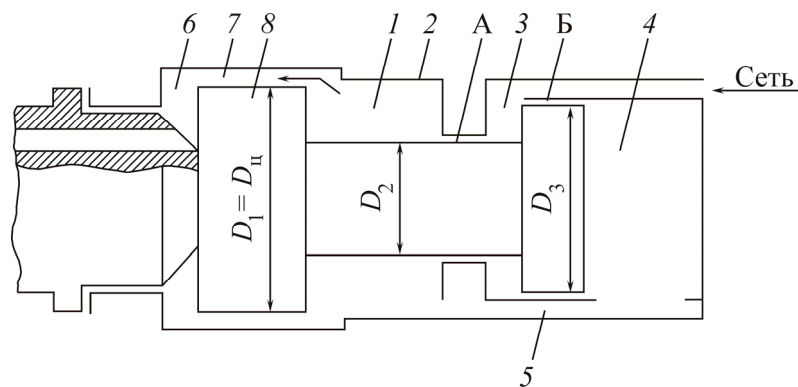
Принципиальная схема погружного пневмоударника: 1 — кольцевая камера рабочего хода; 2 — цилиндр; 3 — камера холостого хода; 4 — торцевая камера рабочего хода; 5 — канал, соединяющий рабочие камеры; 6 — камера атмосферного давления; 7 — выхлопной канал; 8 — ударник;  $D_1 - D_3$  — диаметры ступеней ударника;  $D_{ц}$  — диаметр цилиндра; А и Б — зазоры в подвижных посадках
